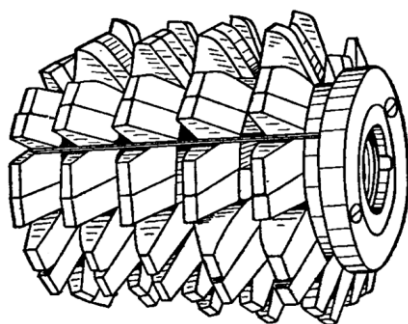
Фреза червячная цельная для нарезания зубьев цилиндрических зубчатых колес
